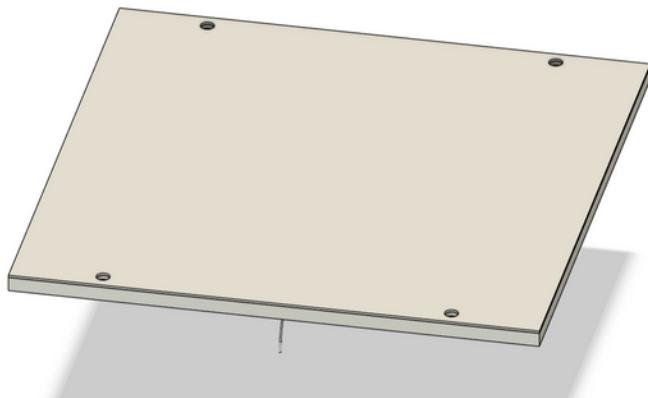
Cama calefactora PCB de aluminio, 300x300x3mm.
